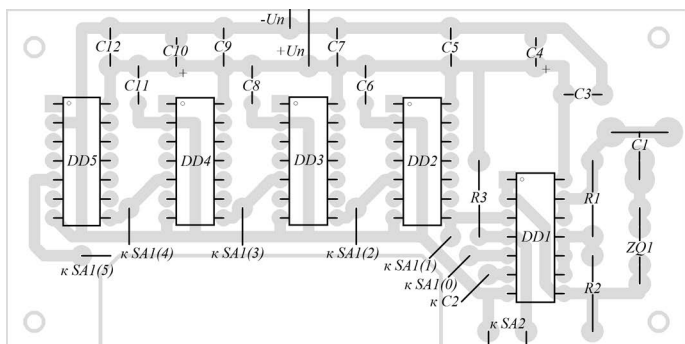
Эскиз монтажной платы кварцевого калибратора. Вид со стороны установки деталей
